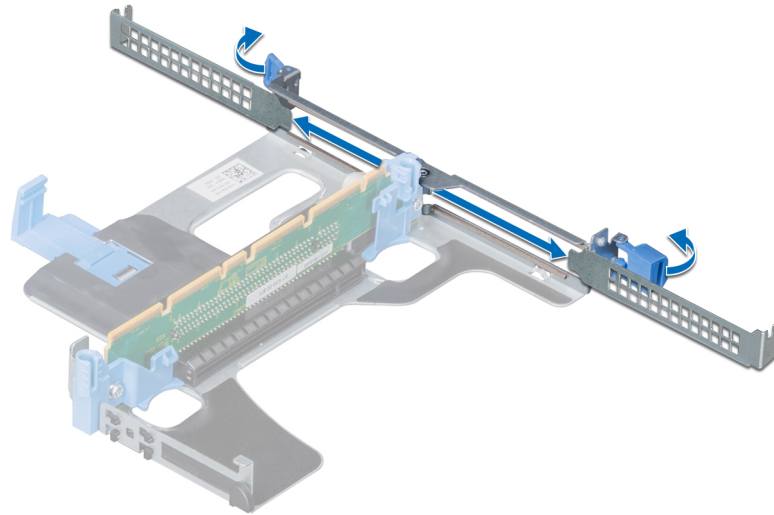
Retrait de la plaque de recouvrement métallique sur la carte de montage 1A
